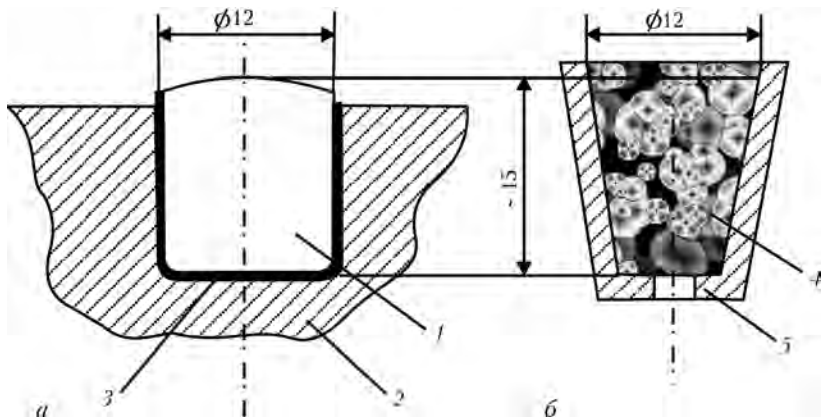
Геометрические параметры отработавших монолитной (а) и дробленой (б) твердосплавных вставок типа В-20 в тигле дериватографа: 1 — твердосплавная вставка; 2 — корпус буровой коронки; 3 — припой Л-63; 4 — дробленая твердосплавная вставка; 5 — корпус тигля дериватографа Q-1500
